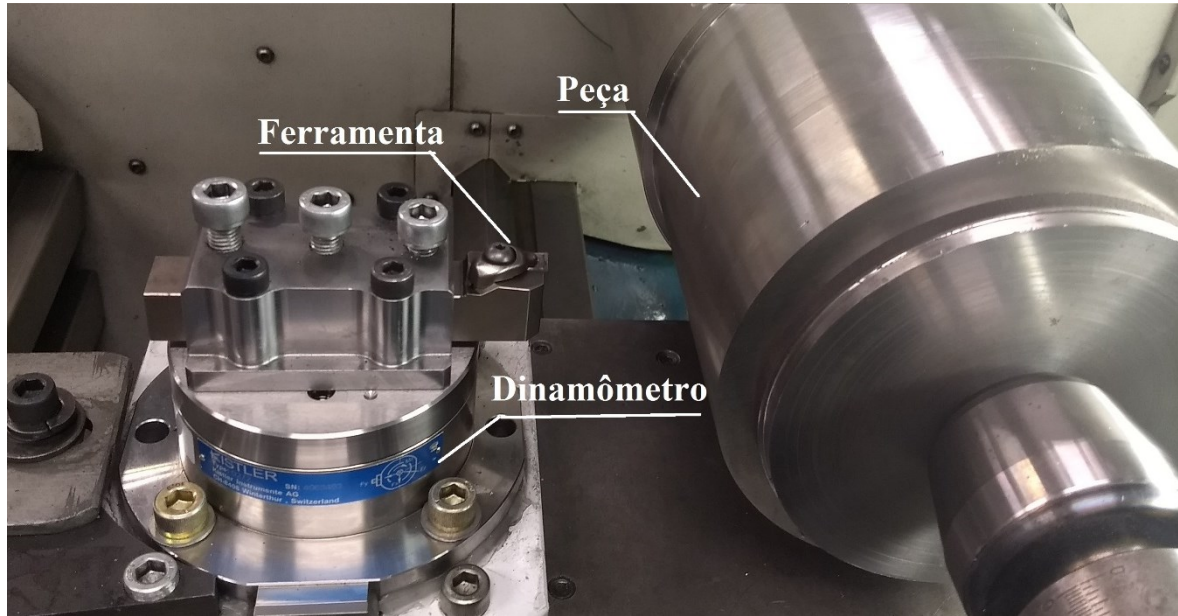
Montagem do dinamômetro para a medição dos componentes da força de usinagem.
